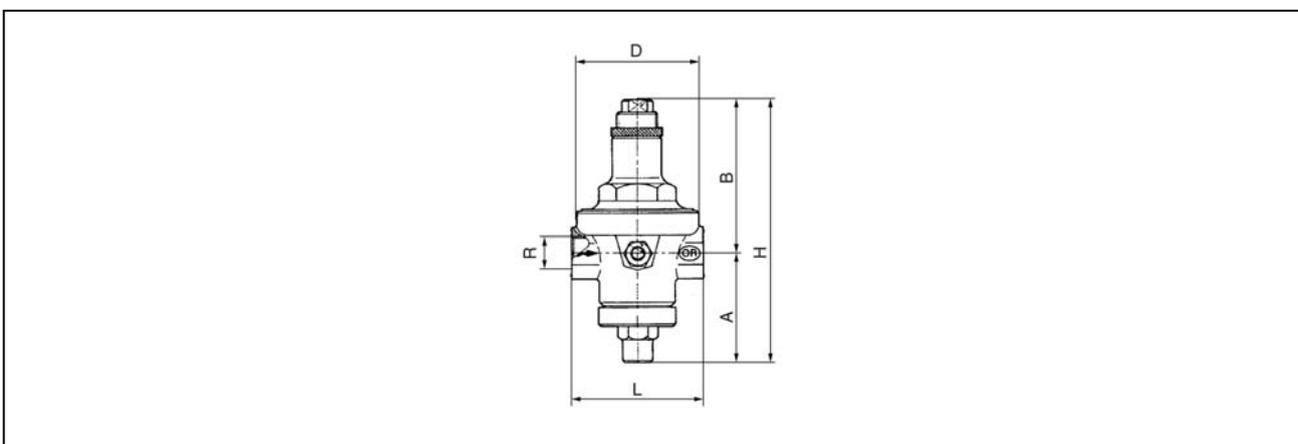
Габаритные и присоединительные размеры клапана типа RP226.
